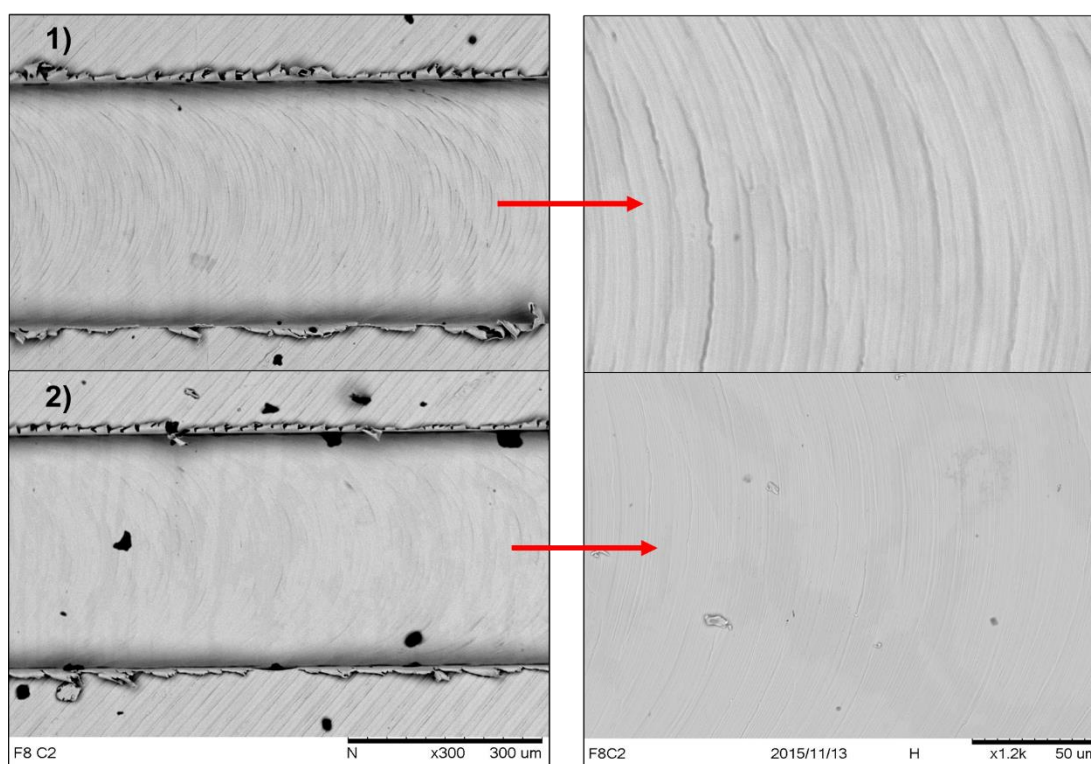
Superfície gerada após usinagem do primeiro (1) e segundo (2) passe ao utilizar fluido de corte
